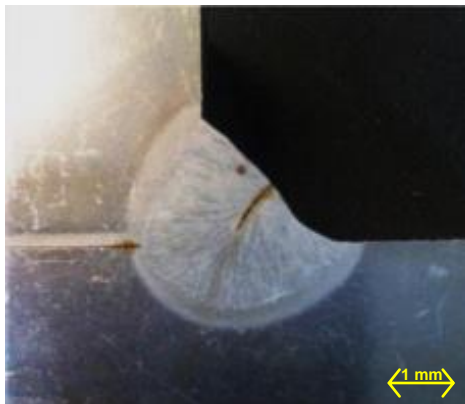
Fractura de garganta en soldadura de filete (28)
